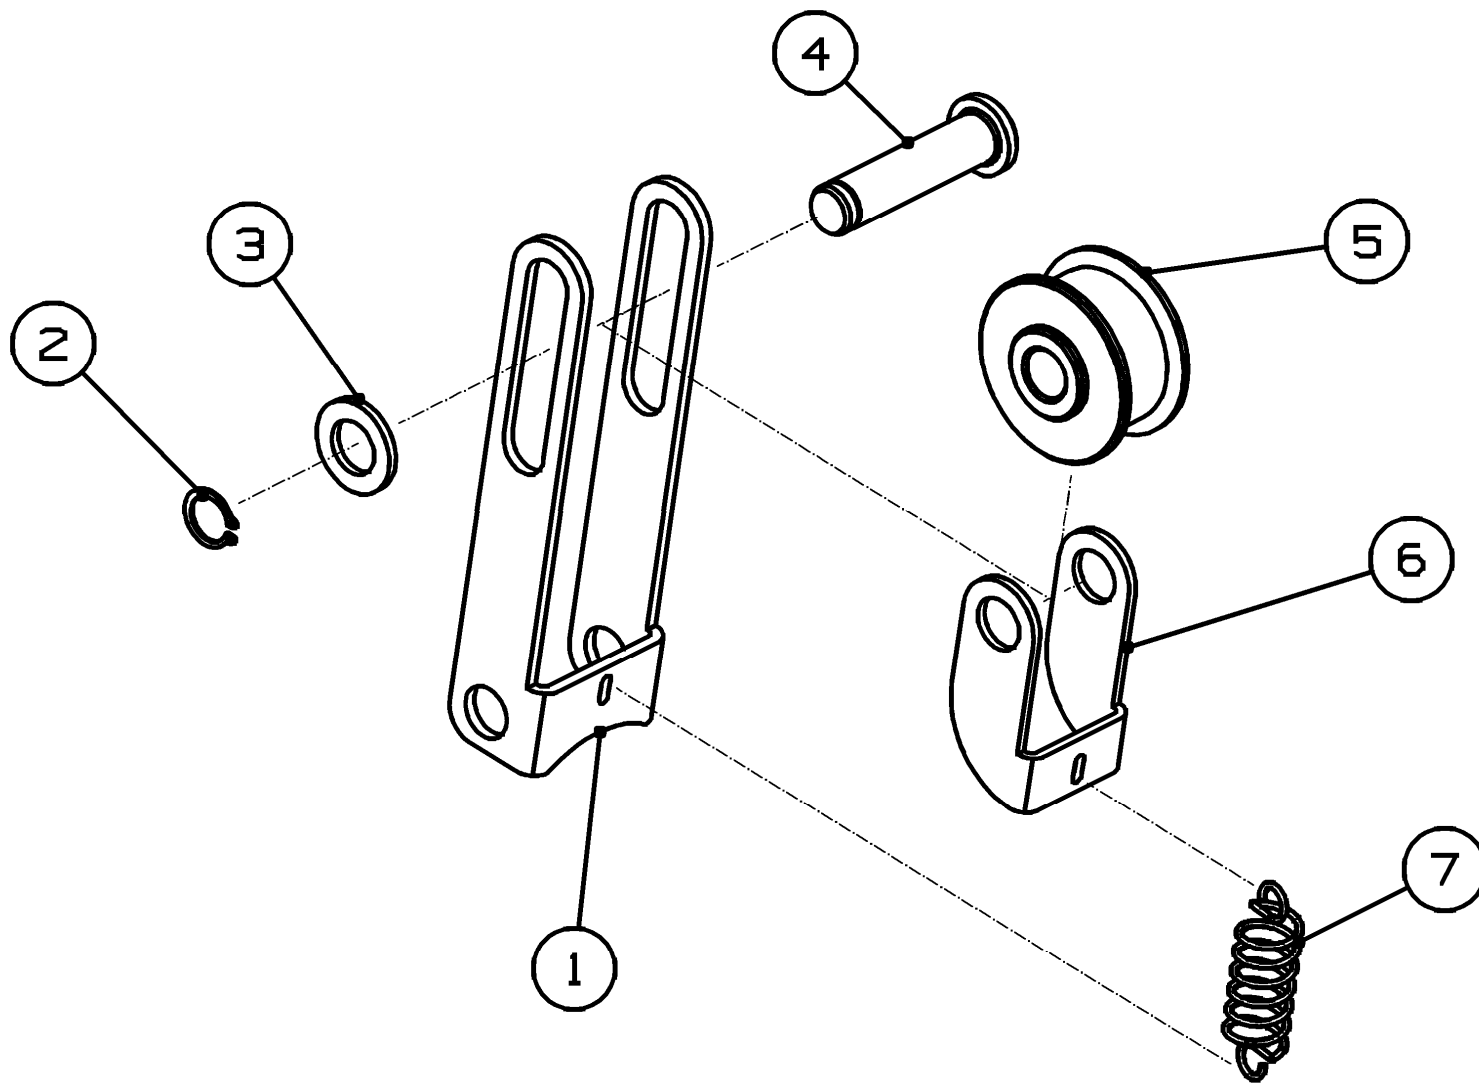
Натяжитель цепи - РА-900.90.20.000
